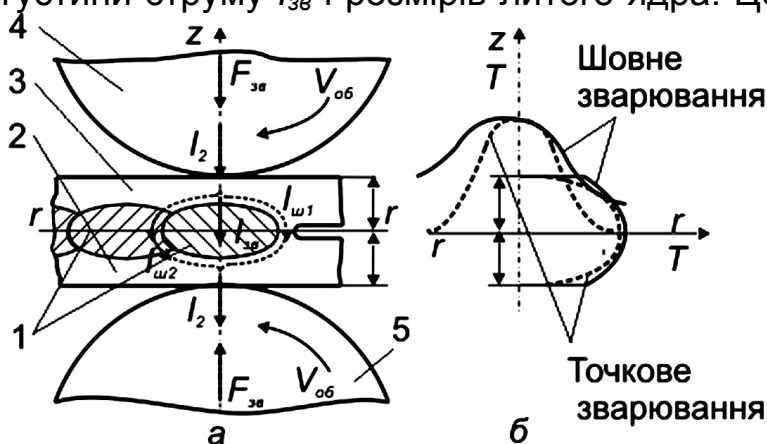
Шовне зварювання: а - шунтування зварювального струму; б - розподіл температур
